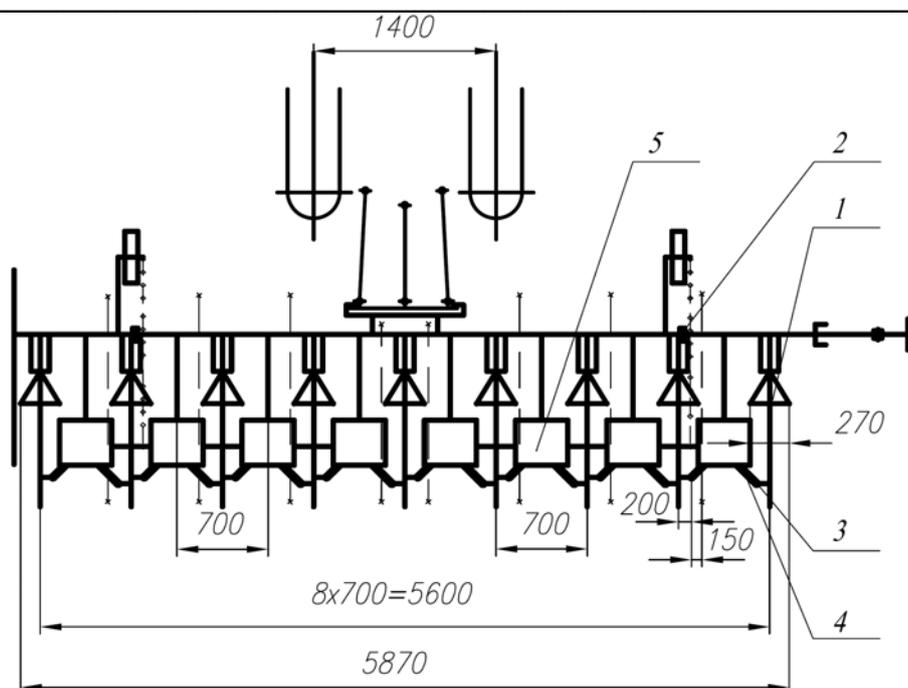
Схема расположения рабочих органов КРН-5,6К с подкормочным приспособлением для междурядий 70см.
